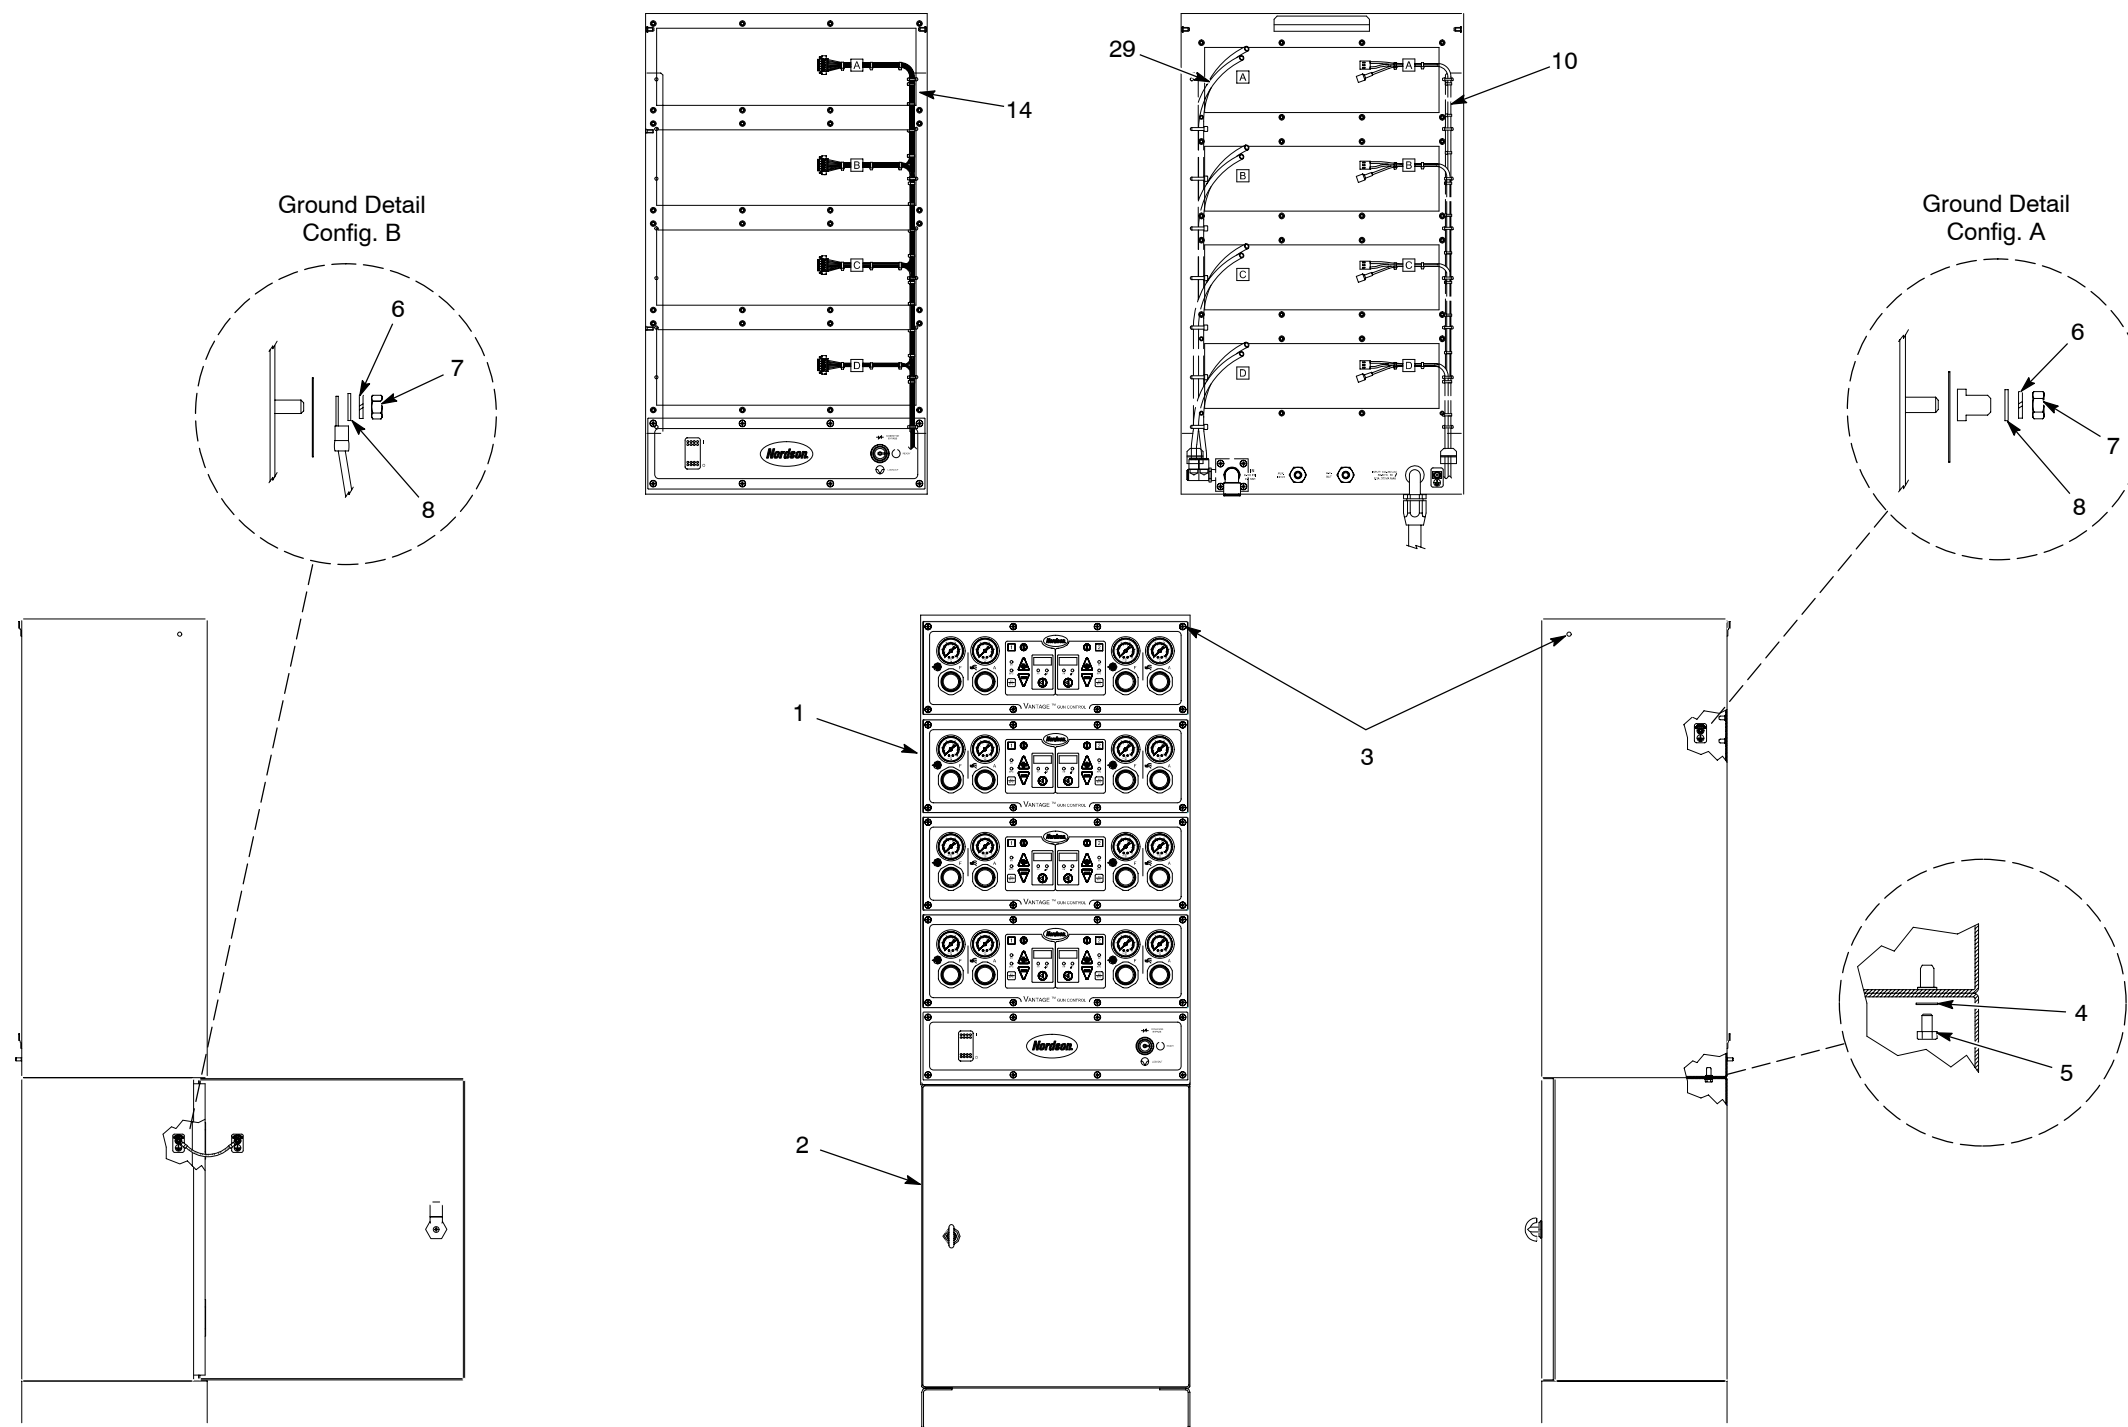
Sistema de control de pistola modular Vantage (1 de 2)
